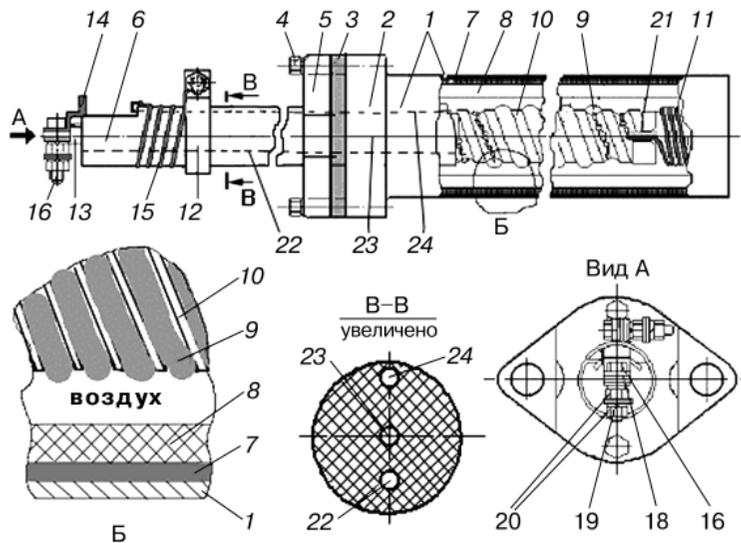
Конструкция высоковольтного нагревателя ННС2-0,5:
